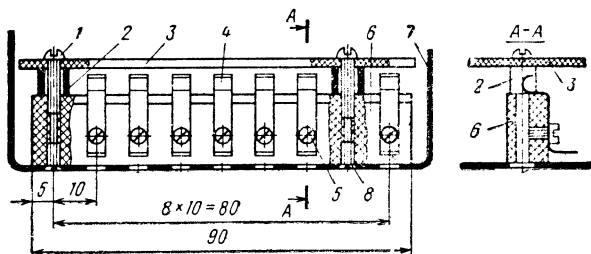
Устройство гнездовой колодки и крепление ее в корпусе вольтметра
